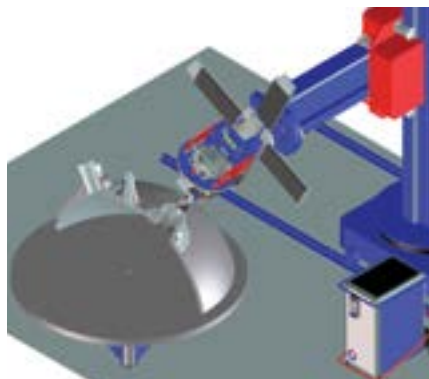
Схема универсальной установки с коллекторной сварочной головкой для наплавки отверстий на закрепленных деталях. Суппорт, на который установлена головка, обеспечивает перемещение. Установка позволяет наплавлять отверстия без необходимости вращать деталь.
